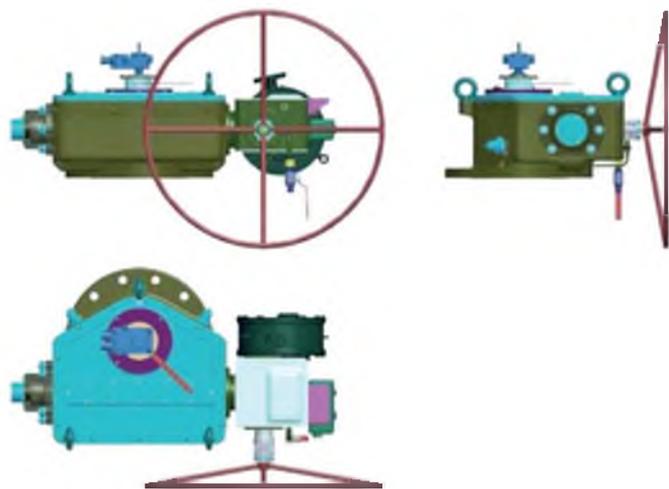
Электропневматический струйно-реактивный привод шарового крана DN 700 PN 100 [2]
